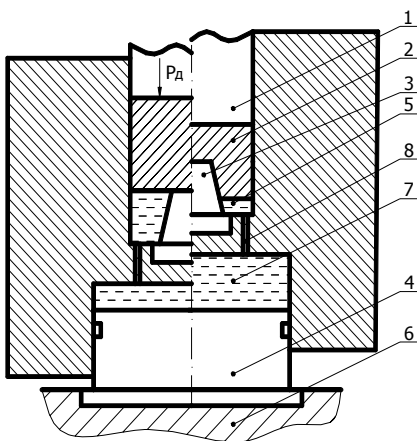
Схема штампу для видавлювання порожнин з протитиском
